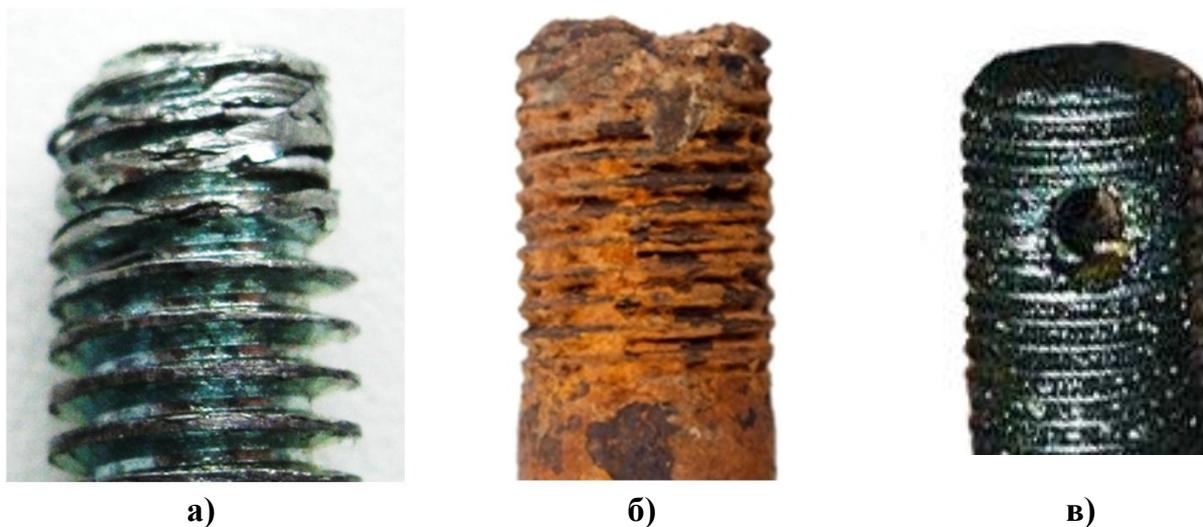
Резьбовая поверхность: а – смятие витков резьбы; б – коррозия резьбовой поверхности; в – витки резьбы с загрязнением
